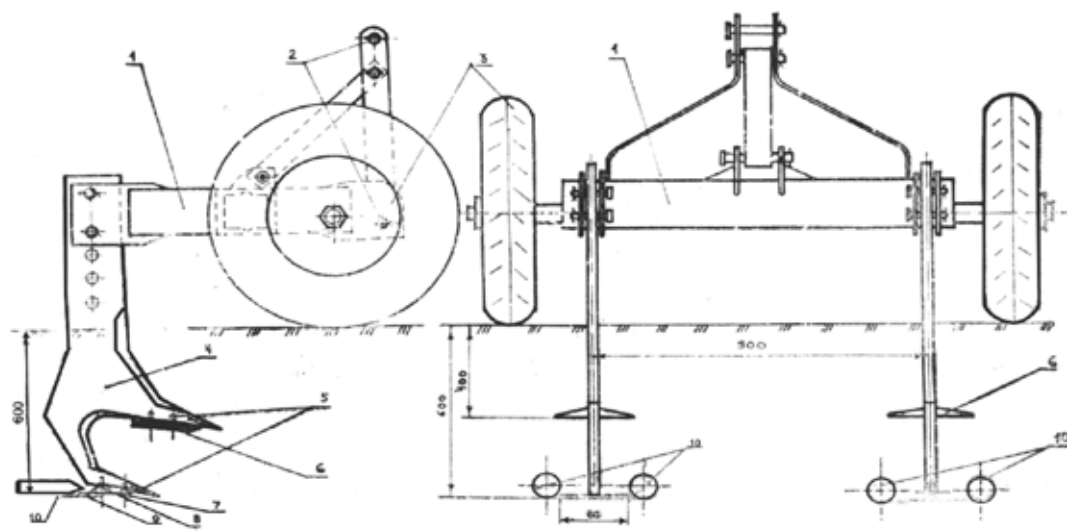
1 – рама; 2 – навеска; 3 – опорное колесо; 4 – вертикальный нож; 5 – зубы ножа; 6 – долота; 7 – проушина; 8 – вертикальный шарнир; 9 – поводка; 10 – кротователи.
